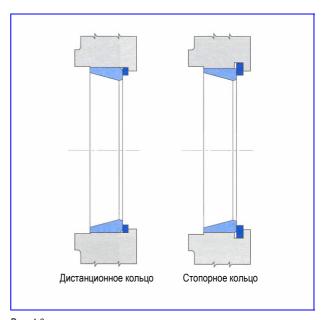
Для увеличения диаметра заплечика корпуса используется отдельный элемент.
